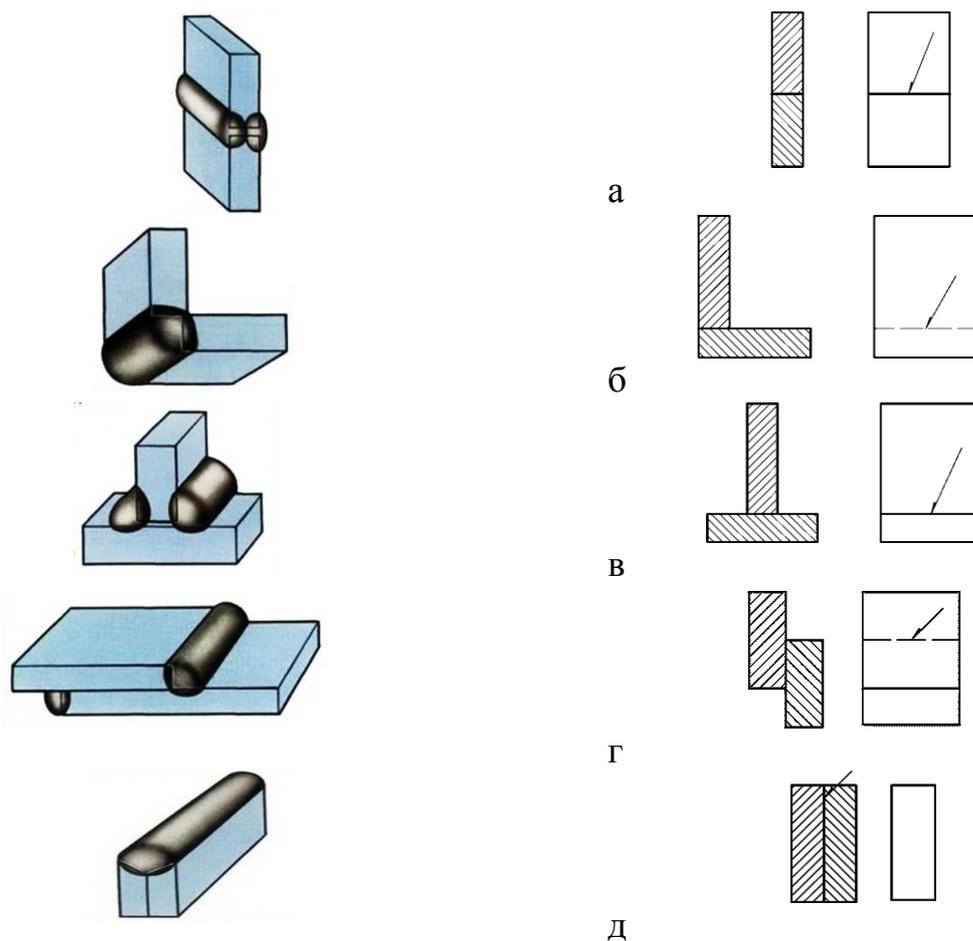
Виды сварных соединений: а-стыковое; б- угловое; в- тавровое; г- нахлесточное; д- торцовое.
